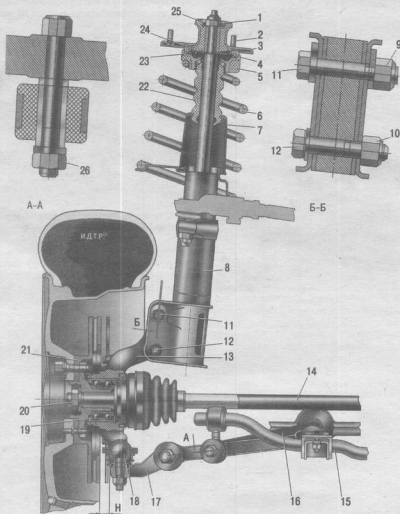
Передняя подвеска в сборе: 1 – гайка крепления верхней опоры стойки; 2 – болт; 3 – верхняя опора стойки передней подвески; 4 – подшипник верхней опоры стойки; 5 – верхняя изоляционная прокладка пружины; 6 – пружина передней подвески; 7 – защитный кожух; 8 – телескопическая стойка в сборе; 9, 10 – гайки крепления стойки к поворотному кулаку; 11 – болт с эксцентриком; 12 – болт; 13 – поворотный кулак; 14 – вал привода переднего колеса; 15 – штанга стабилизатора; 16 – растяжка; 17 – рычаг; 18 – шаровая опора; 19 – ступица; 20 – гайка крепления ступицы; 21 – тормозной диск; 22 – буфер хода сжатия передней подвески; 23 – верхняя чашка пружины; 24 – ограничитель хода сжатия верхней опоры стойки; 25 – ограничитель хода верхней опоры стойки; 26 – гайка крепления стойки стабилизатора; Н – контрольный размер
